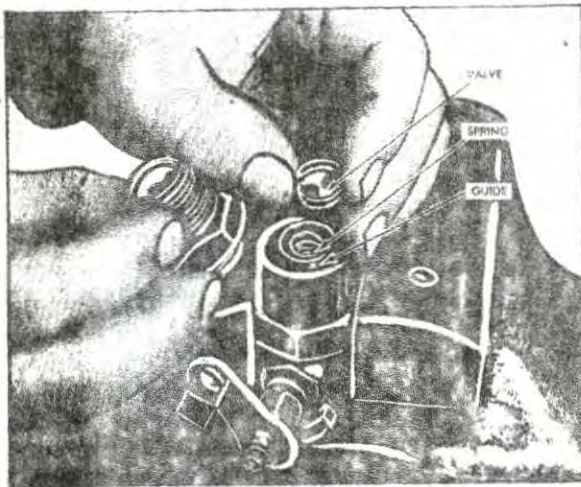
Montaje del conjunto de válvula de retención de alimentación de combustible.
